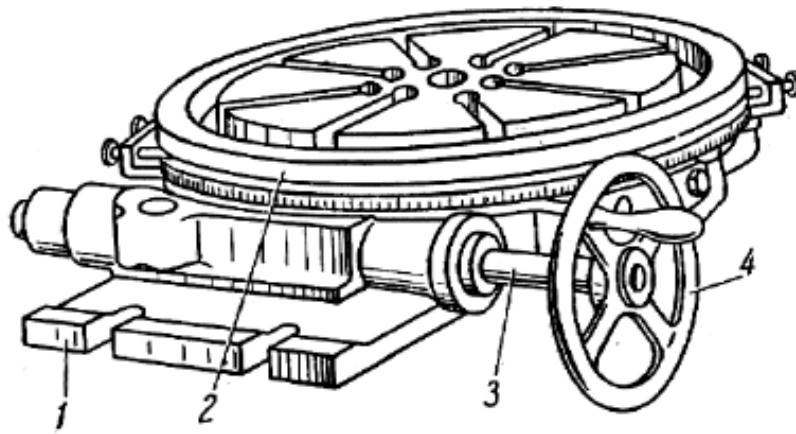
Поворотний стіл: 1 – плита; 2 – поворотна частина стола; 3 – вал; 4 - маховик
